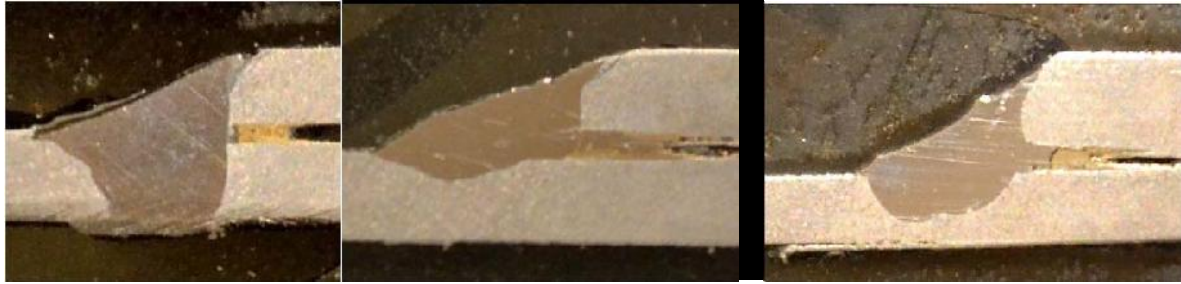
Макрошлифы паяно-сварных соединений
